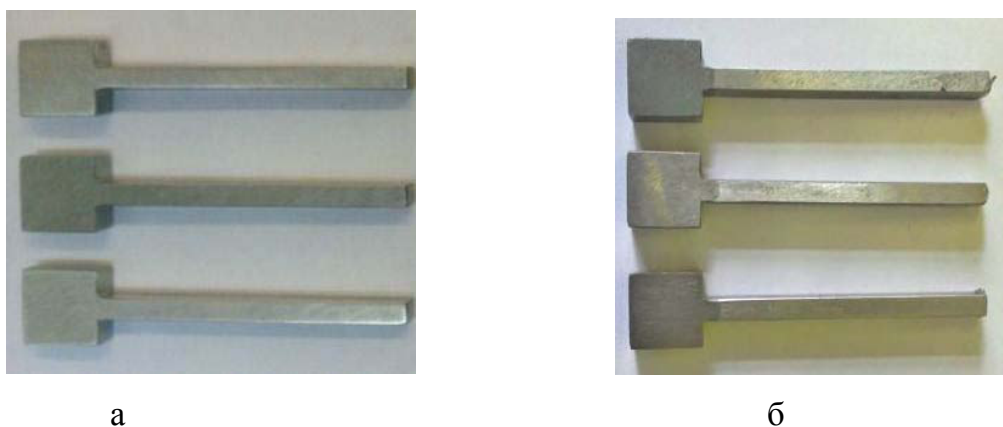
Образцы на питтинговую коррозию до испытаний (а) и после испытаний (б) металла, наплавленного сварочной проволокой марки Св-МНЖМцТК40-1-1-0,3-0,1
